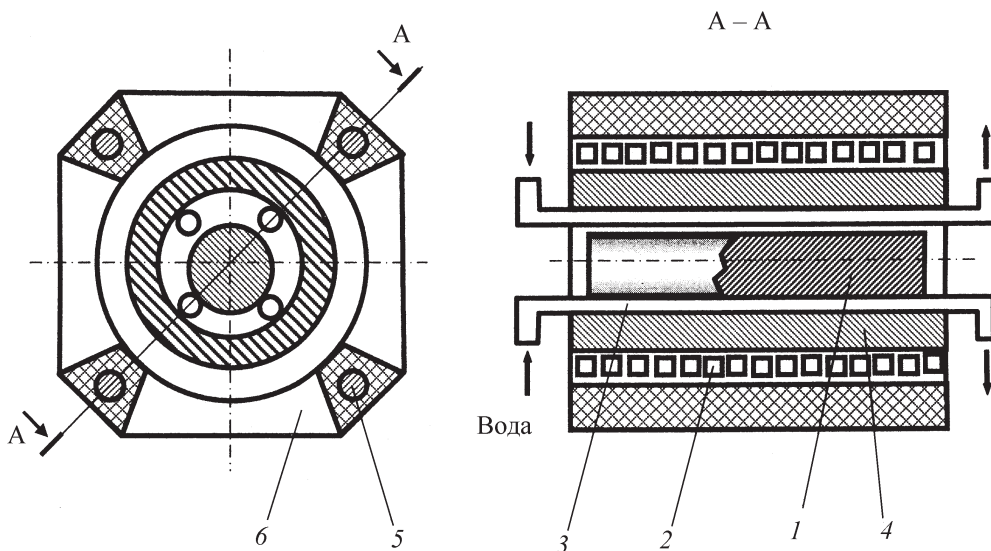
Схема индуктора для нагрева цилиндрических заготовок:
